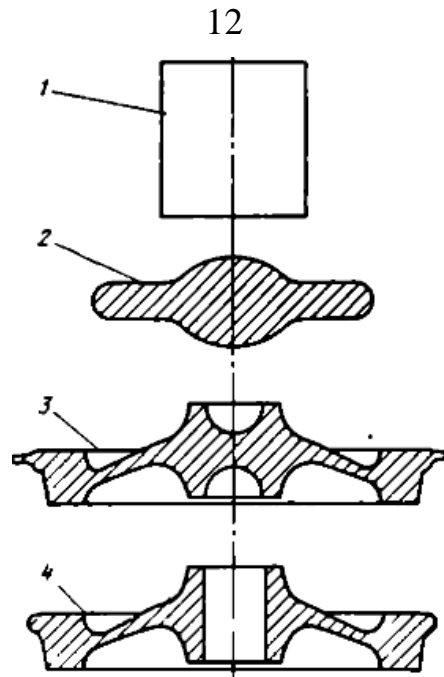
Схема производства штампованных колес на заводе фирмы «Chambersburg» США: 1 - заготовка, 2 - заготовка после осадки и раздачи, 3 - заготовка после формовки, 4 - заготовка после прошивки отверстия
